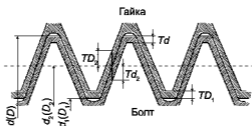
Схема расположения полей допусков резьбы
